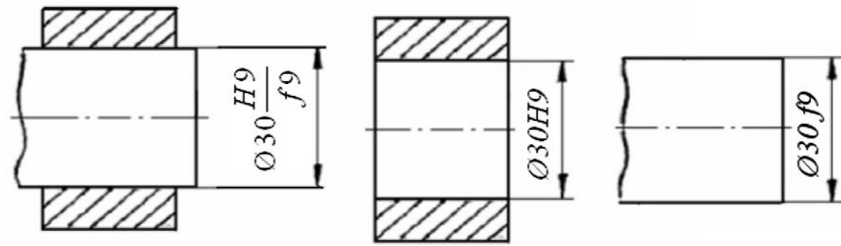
Схема розташування інтервалів допусків
